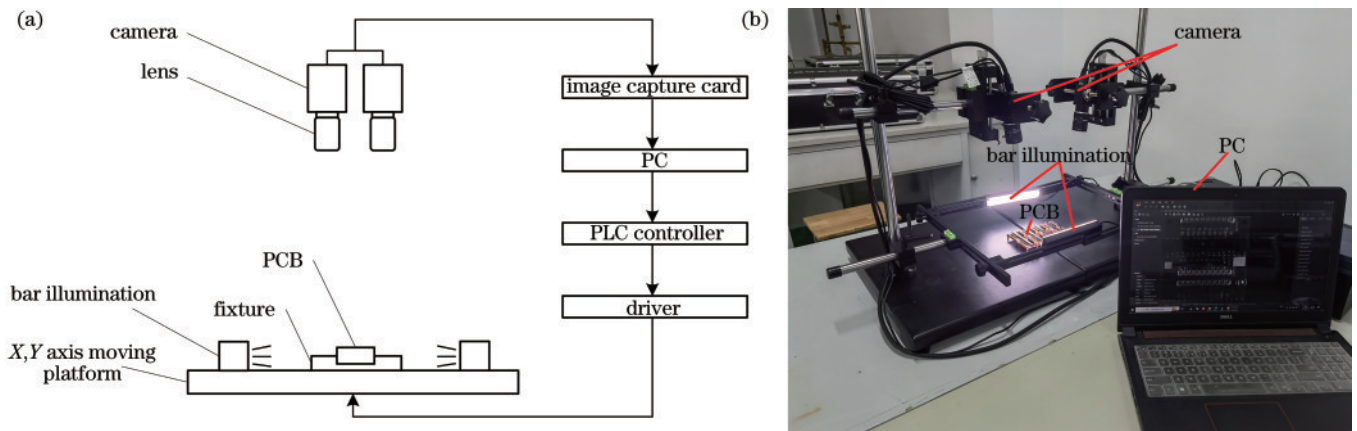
PCB PIN双目视觉检测系统。(a)硬件结构;(b)实验平台
